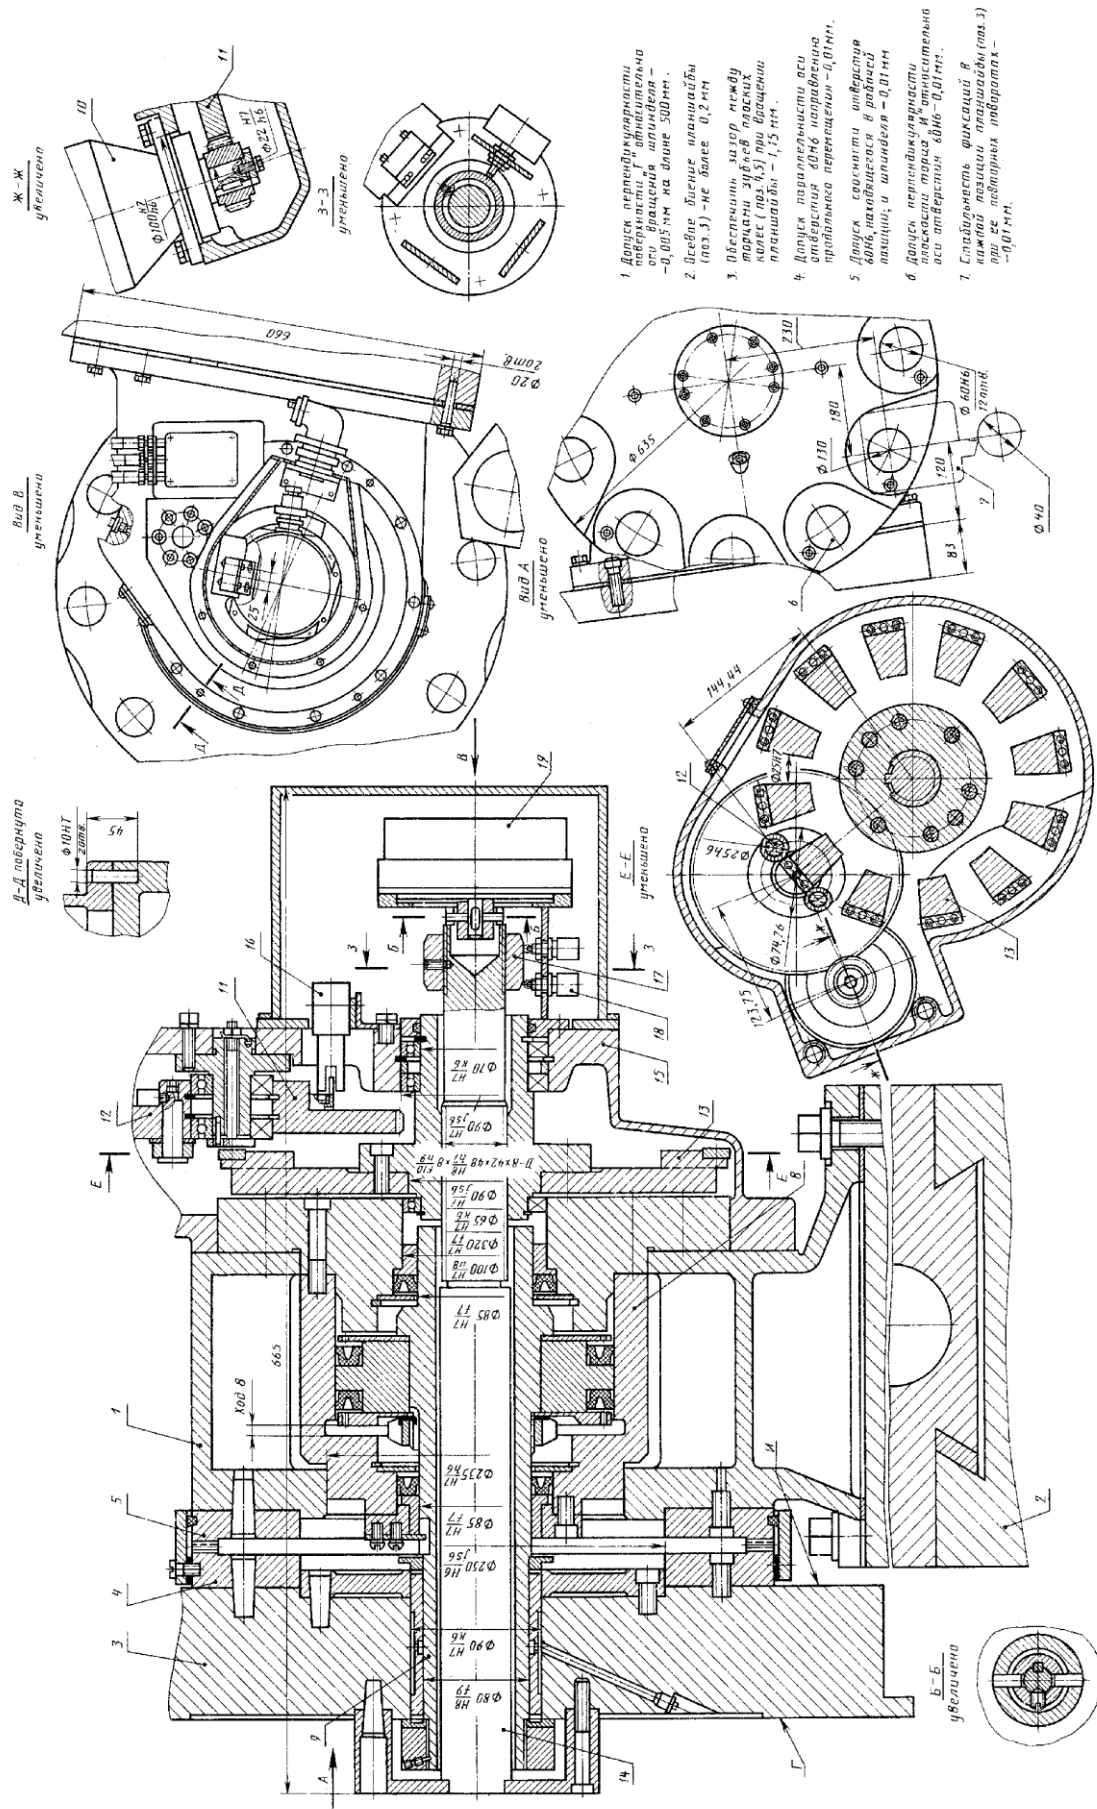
Механизм револьверной головки верстака 1740РФЗ
